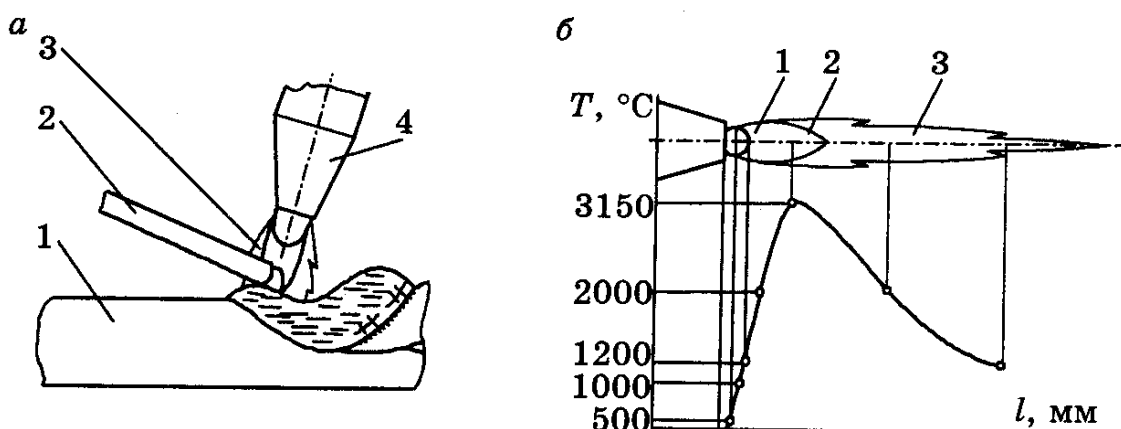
Схемы процесса газовой сварки (а) и ацетилено-кислородного пламени (б)
